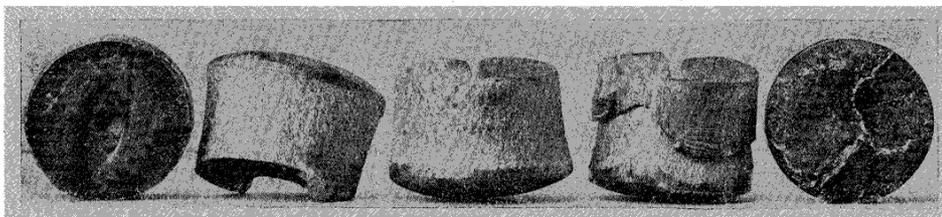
à 226. — Photographies de débouchures obtenues avec le poinçon en forme de double hélice.
